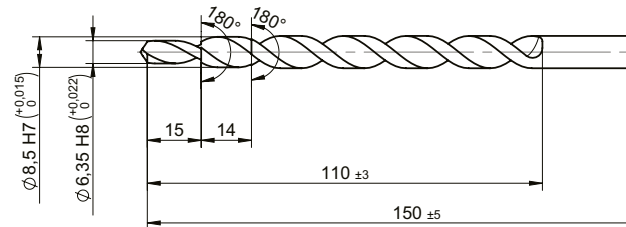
Stufenbohrer Typ 1337A für Montagenippel M10x1
